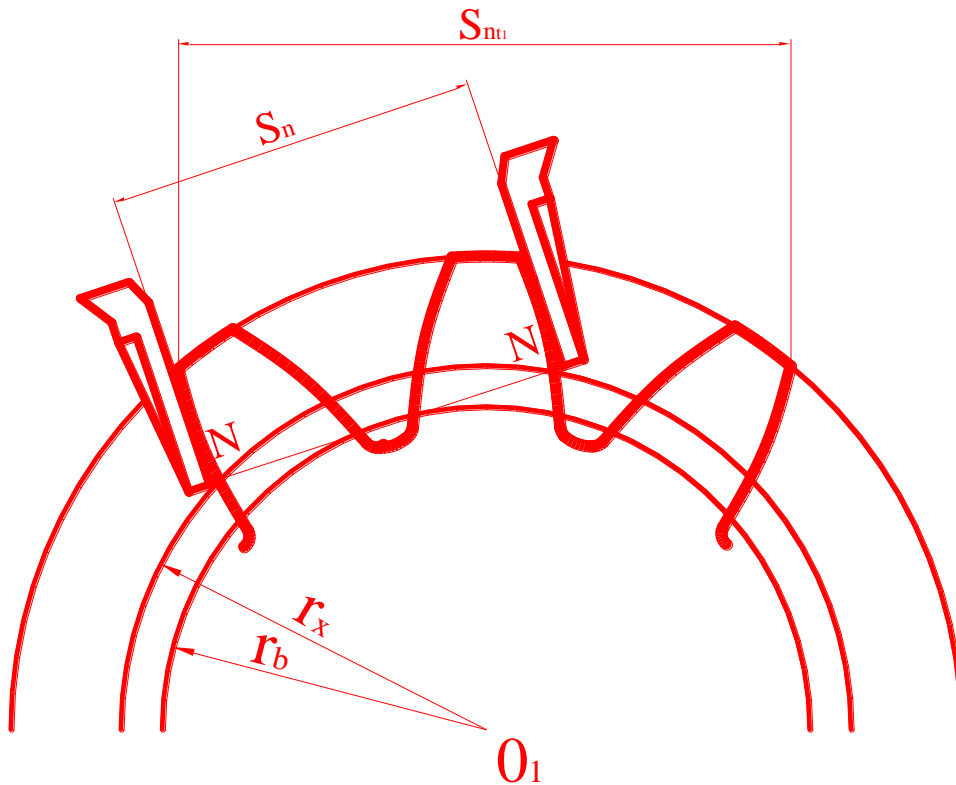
Установлення штангенциркуля при обмірюванні зубчастого колеса
